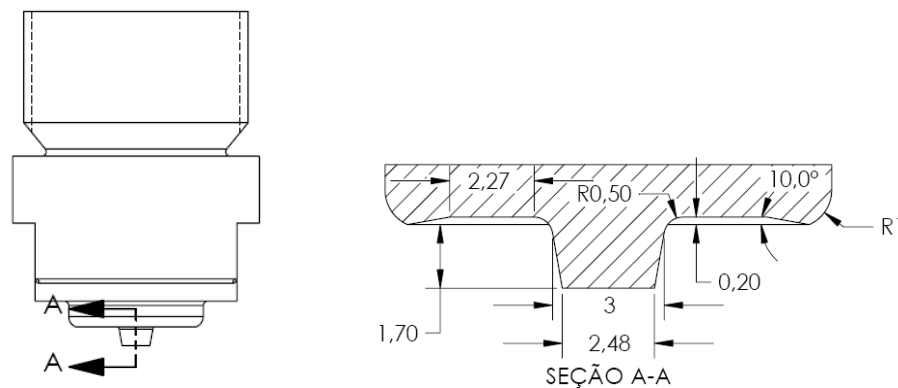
Detalhes do projeto da ferramenta com ombro côncavo e pino de 1,7 mm. O pino é apenas 0,1 mm mais curto que a espessura da chapa utilizada.
